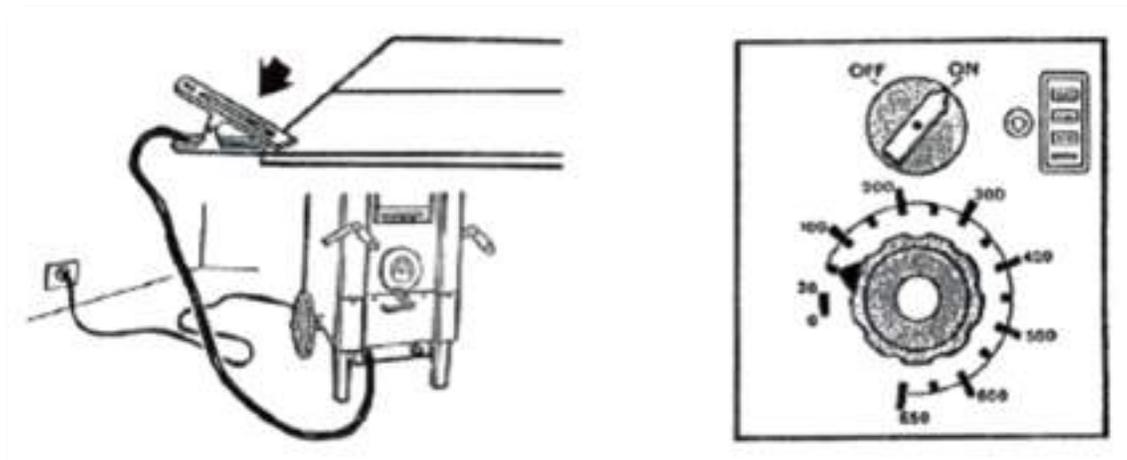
Ligação do equipamento de soldadura e regulação da Intensidade de soldadura.
